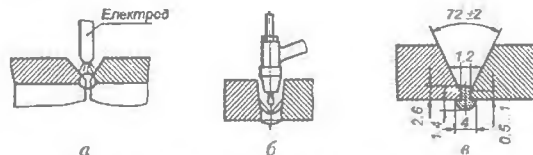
Способи зварювання кореневого шару «на вазі»:
